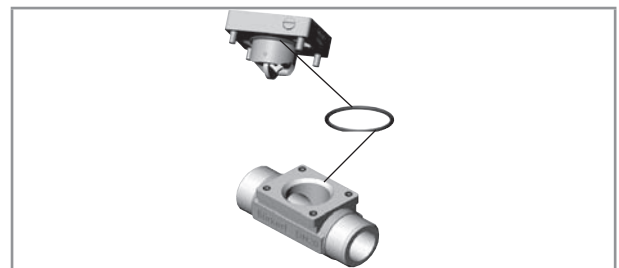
Dichtungsposition bei einem Fitting S030 HT
